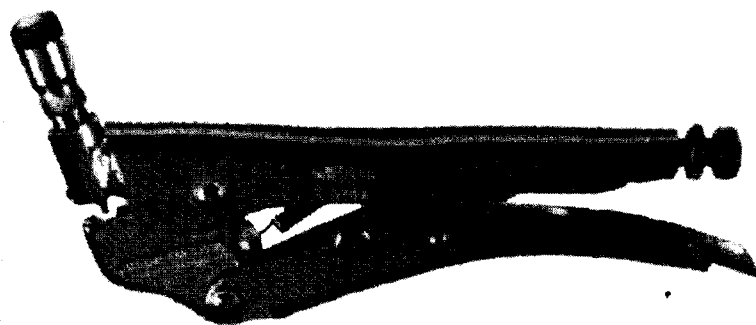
Шипцы-проколка 14210 для установки штуцера с клапаном Шредера
